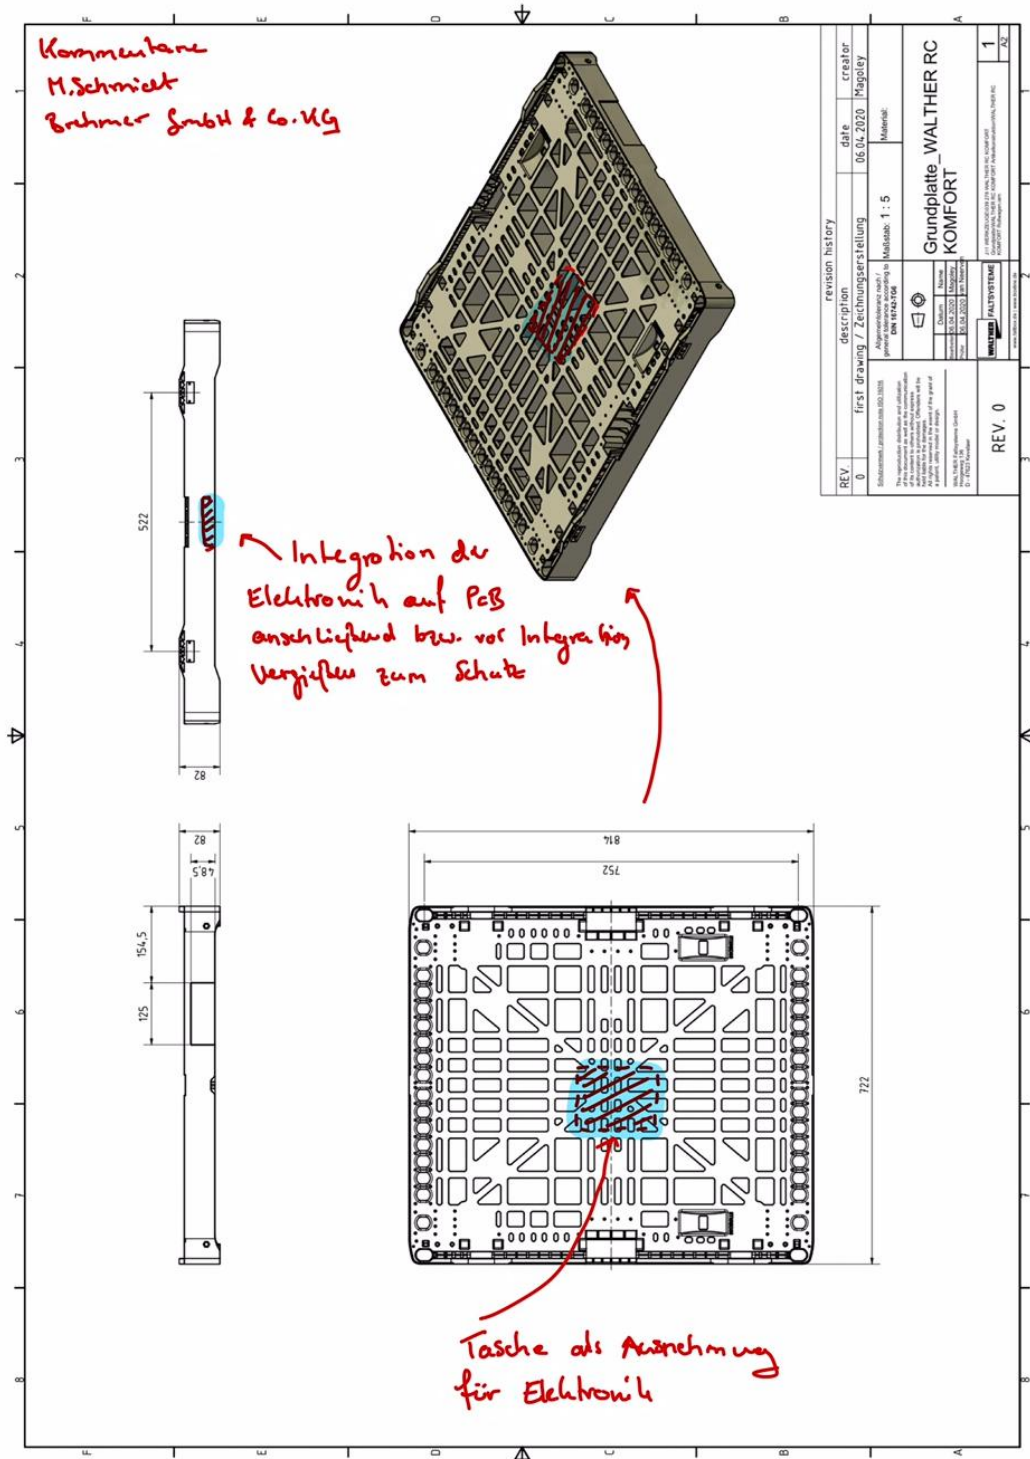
Prinzipskizze Mehrwegladungsträger - Integration der Elektronik
